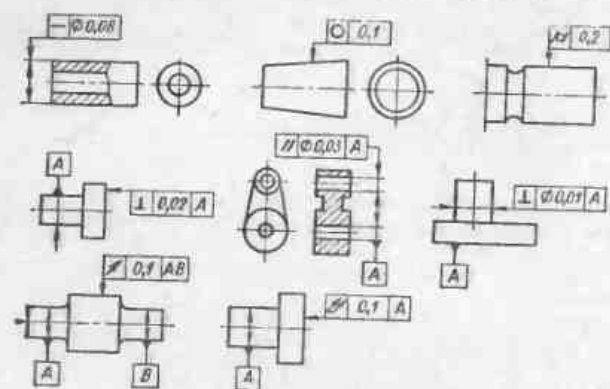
Примеры обозначения допусков формы и расположения поверхностей на чертежах
